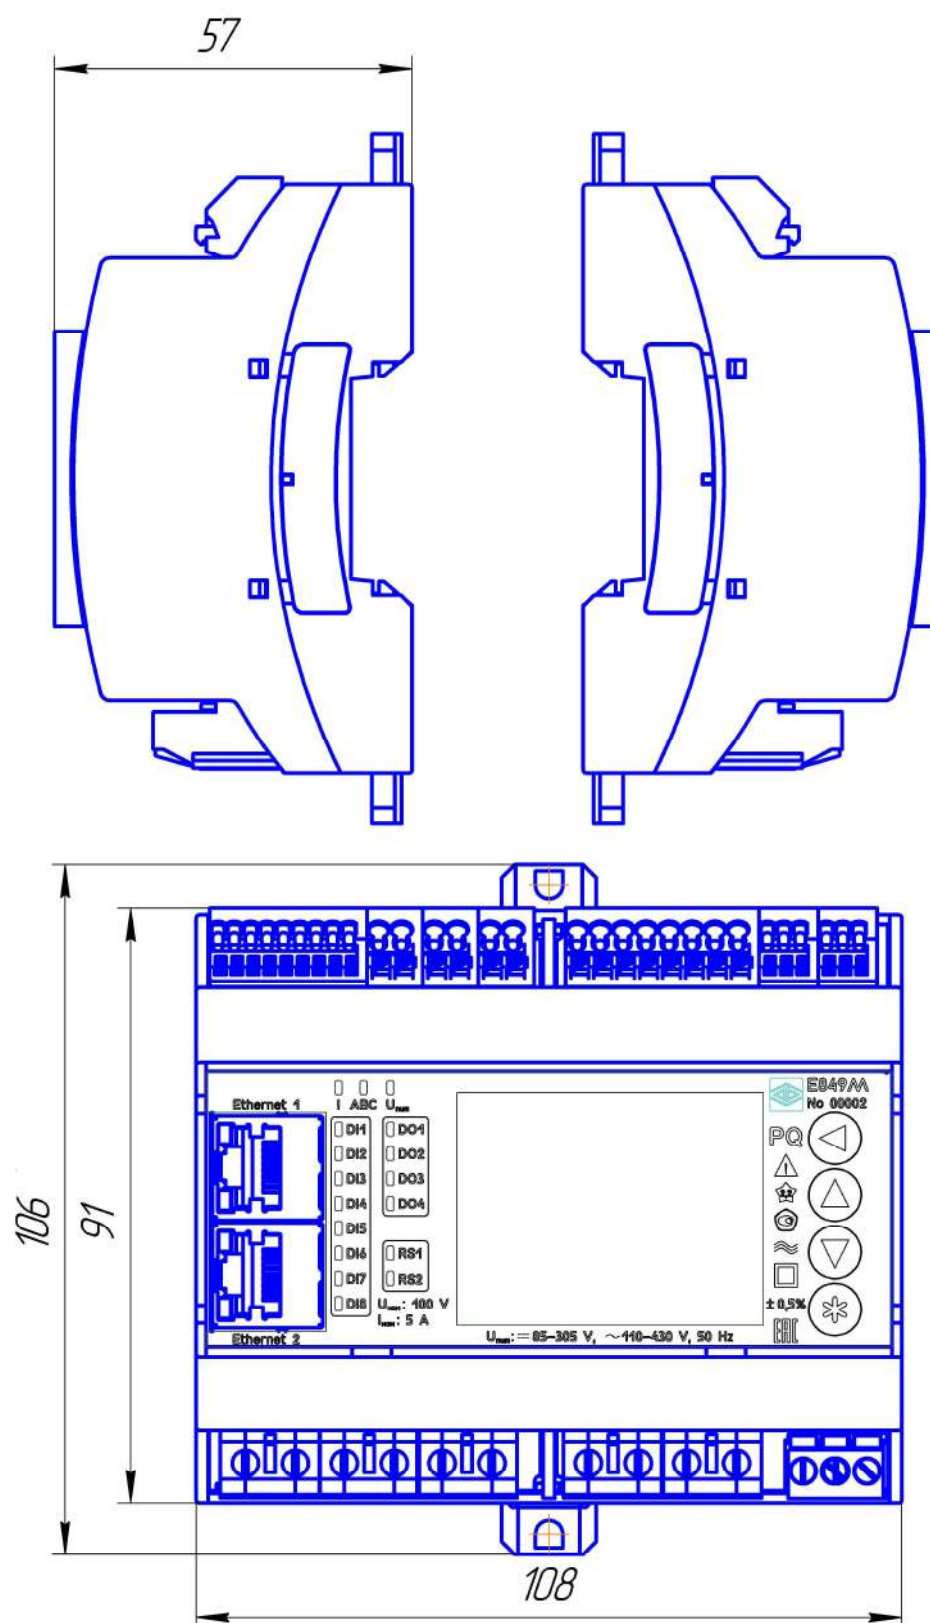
Общий вид, габаритные и установочные размеры (в мм)
